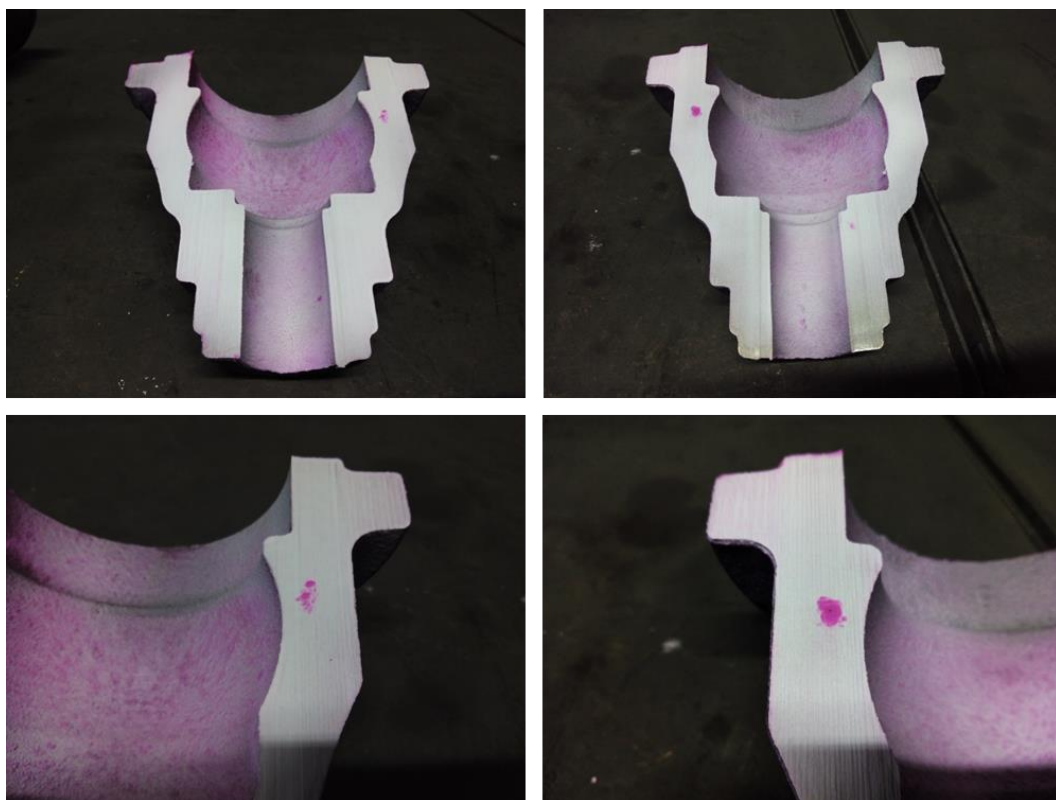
Foto da peça 2, cortada segundo o plano de separação, depois do ensaio de Líquidos Penetrantes.
